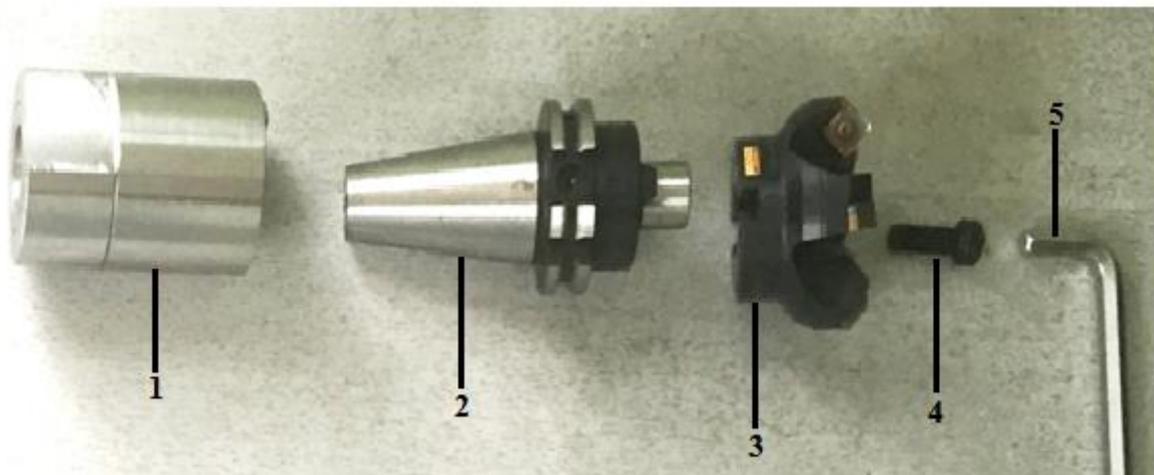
Сборка оправок для насадных фрез и торцевых фрез: 1 - устройство для монтажа захватного болта; 2 - оправка ; 3 - фреза ; 4 - винт оправки; 5 - ключ для оправки.
